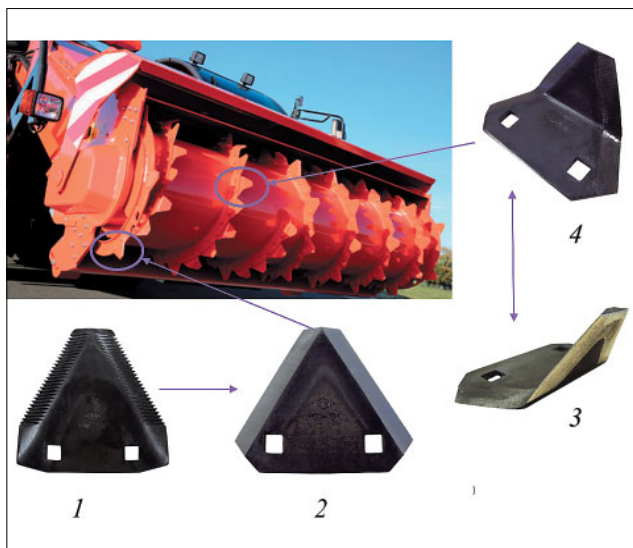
Фрезерный рабочий орган самоходных смесителей-раздатчиков корма KUHN и используемые на нем ножи: 1 – зубчатый треугольный нож; 2 – треугольный нож; 3 – угловой нож с покрытием карбида вольфрама; 4 – угловой нож. Источник: <https://www.kuhn.ru>, каталоги техники для животноводства фирмы KUHN
